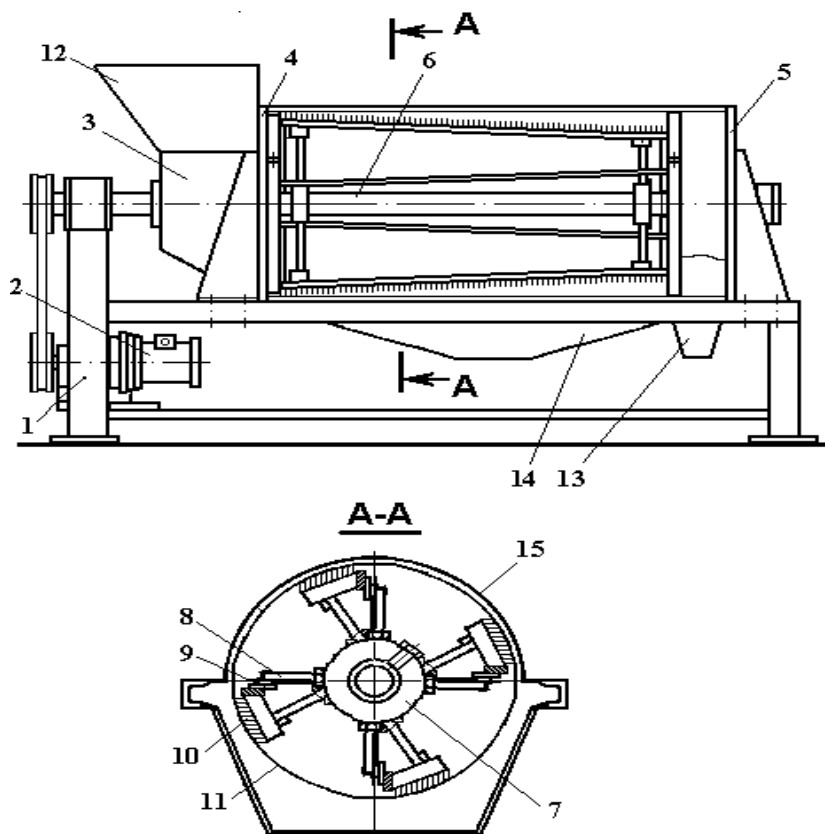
Конструктивно-технологічна схема щіткового роторного просіювача: 1 - рама; 2 - привод; 3 - корпус; 4, 5 - боковини; 6 - вал; 7 - бобишка; 8 - палець; 9 - пластина; 10 - щітка; 11 - сито; 12 - завантажувальна горловина; 13 - вивантажувальна горловина; 14 - вивантажувальне вікно; 15 – кожух
